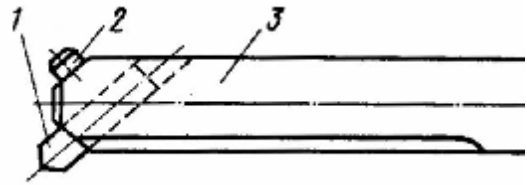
Расточной резец, закрепляемый в оправке: 1- резец, 2-винт крепления резца, 3- державка
